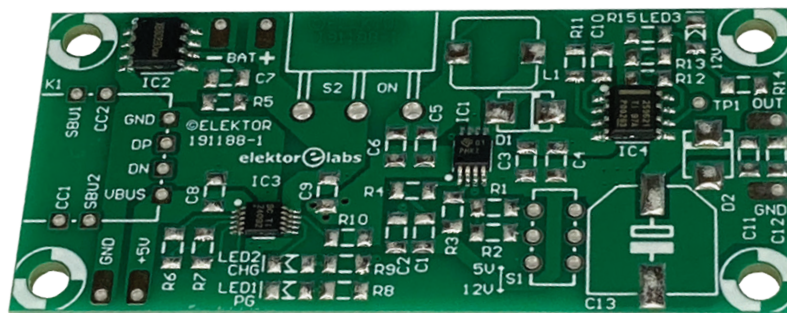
Circuit imprimé fabriqué avec le masque de soudure erroné.
